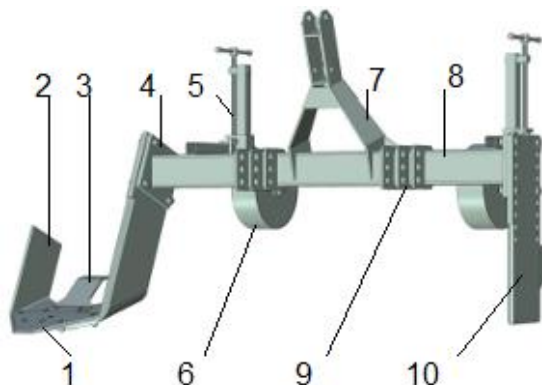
Викопувальний плуг ВПН–2: 1 – леміш; 2 – боковина; 3 – розпушувач; 4 – стояки; 5 – гвинтовий механізм; 6 – опорне колесо; 7 – начіпний механізм; 8 – рама; 9 – кріплення; 10 – ніж стійкості
